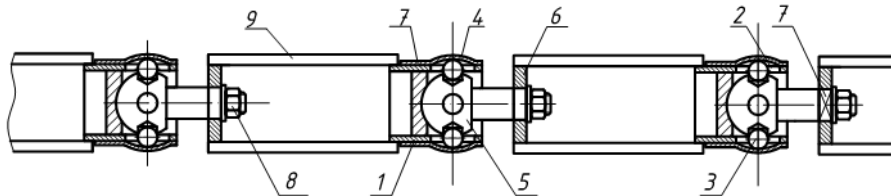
Конструктивна схема гвинтового секційного робочого органу
